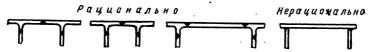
Рациональные формы алюминиевых сварных деталей
